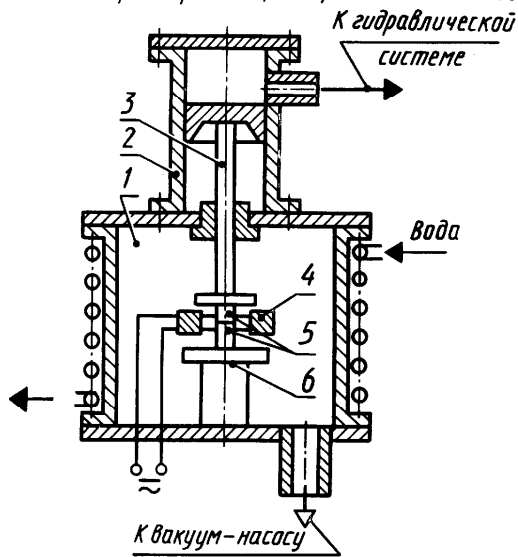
Принципиальная схема установки для диффузионной сварки в вакууме
